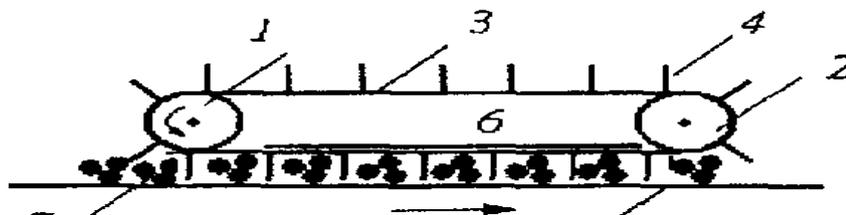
Сжатия скребкового транспортера: 1- механизм привода цепной передачи; 2 - механизм натяжения цепной передачи; 3 - бесконечная цепная передача; 4 - скребок; 5 - опорная поверхность продукта; 6 - опорная поверхность цепной передачи; 7 – продукт.
